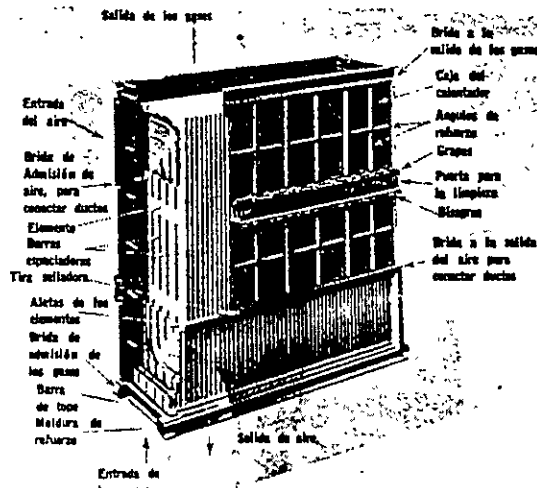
Precalentador de aire por celdas. (Combustion Engineering)
